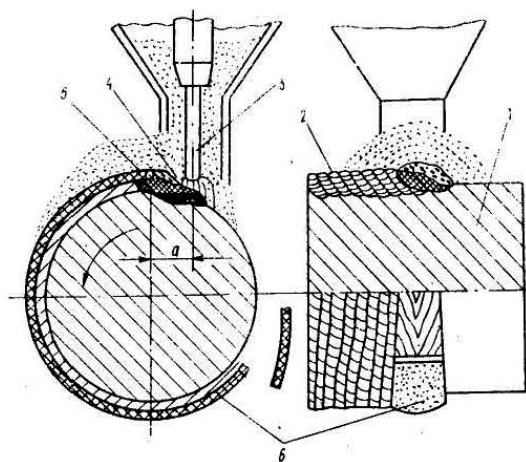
Схема нанесення покриття під шаром флюсу: 1 - виріб; 2 - наплавлений метал; 3 - електрод; 4 - ванна рідкого металу; 5 - плавлений шлак; 6 - шлакова кірка; а - зсув з зеніту.
